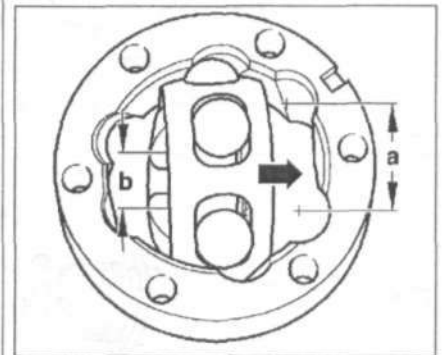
При установке проследите за тем, чтобы широкая сторона «а» корпуса шарнира была совмещена с узкой стороной «b» на ступице.
